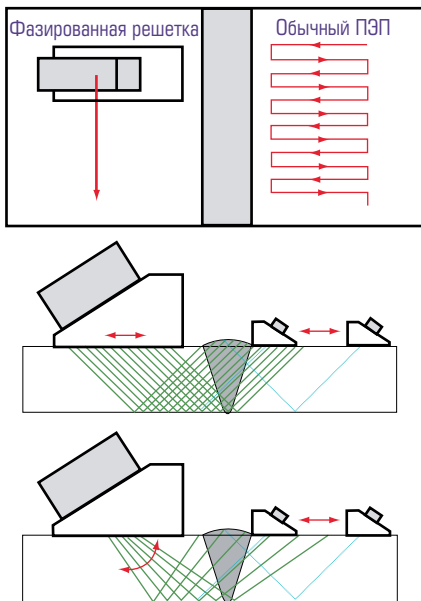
Высокопроизводительный контроль сварного шва с помощью УЗФР
